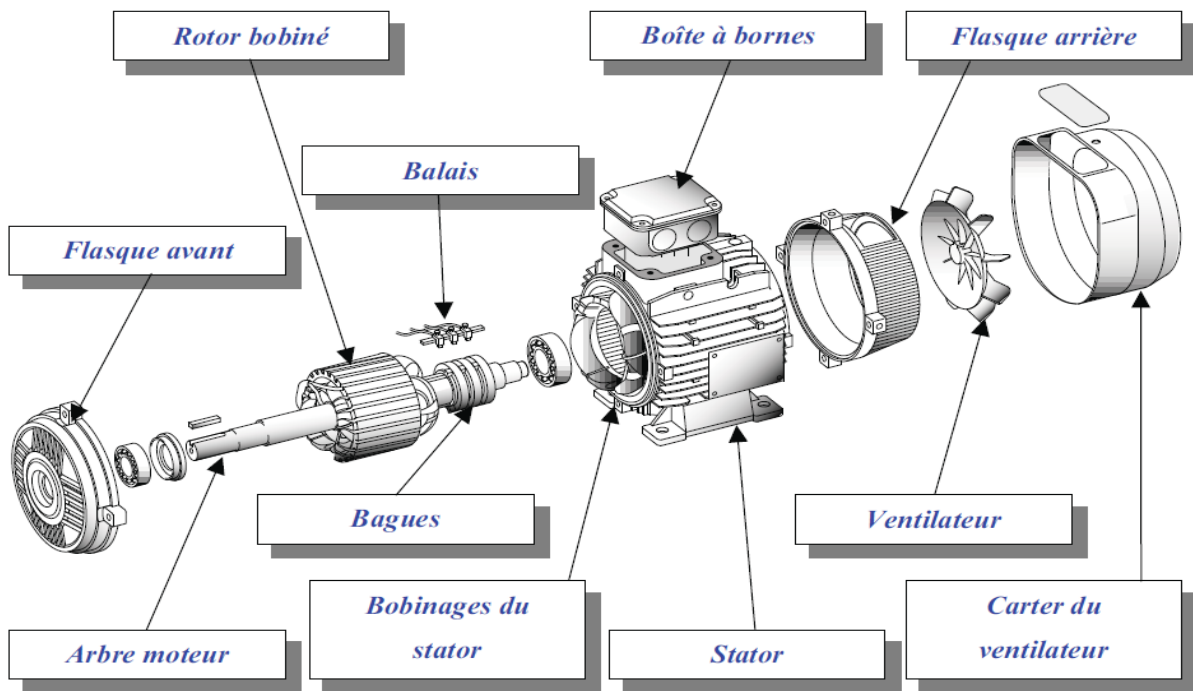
Vue éclatée d'une machine asynchrone triphasée à rotor bobiné
